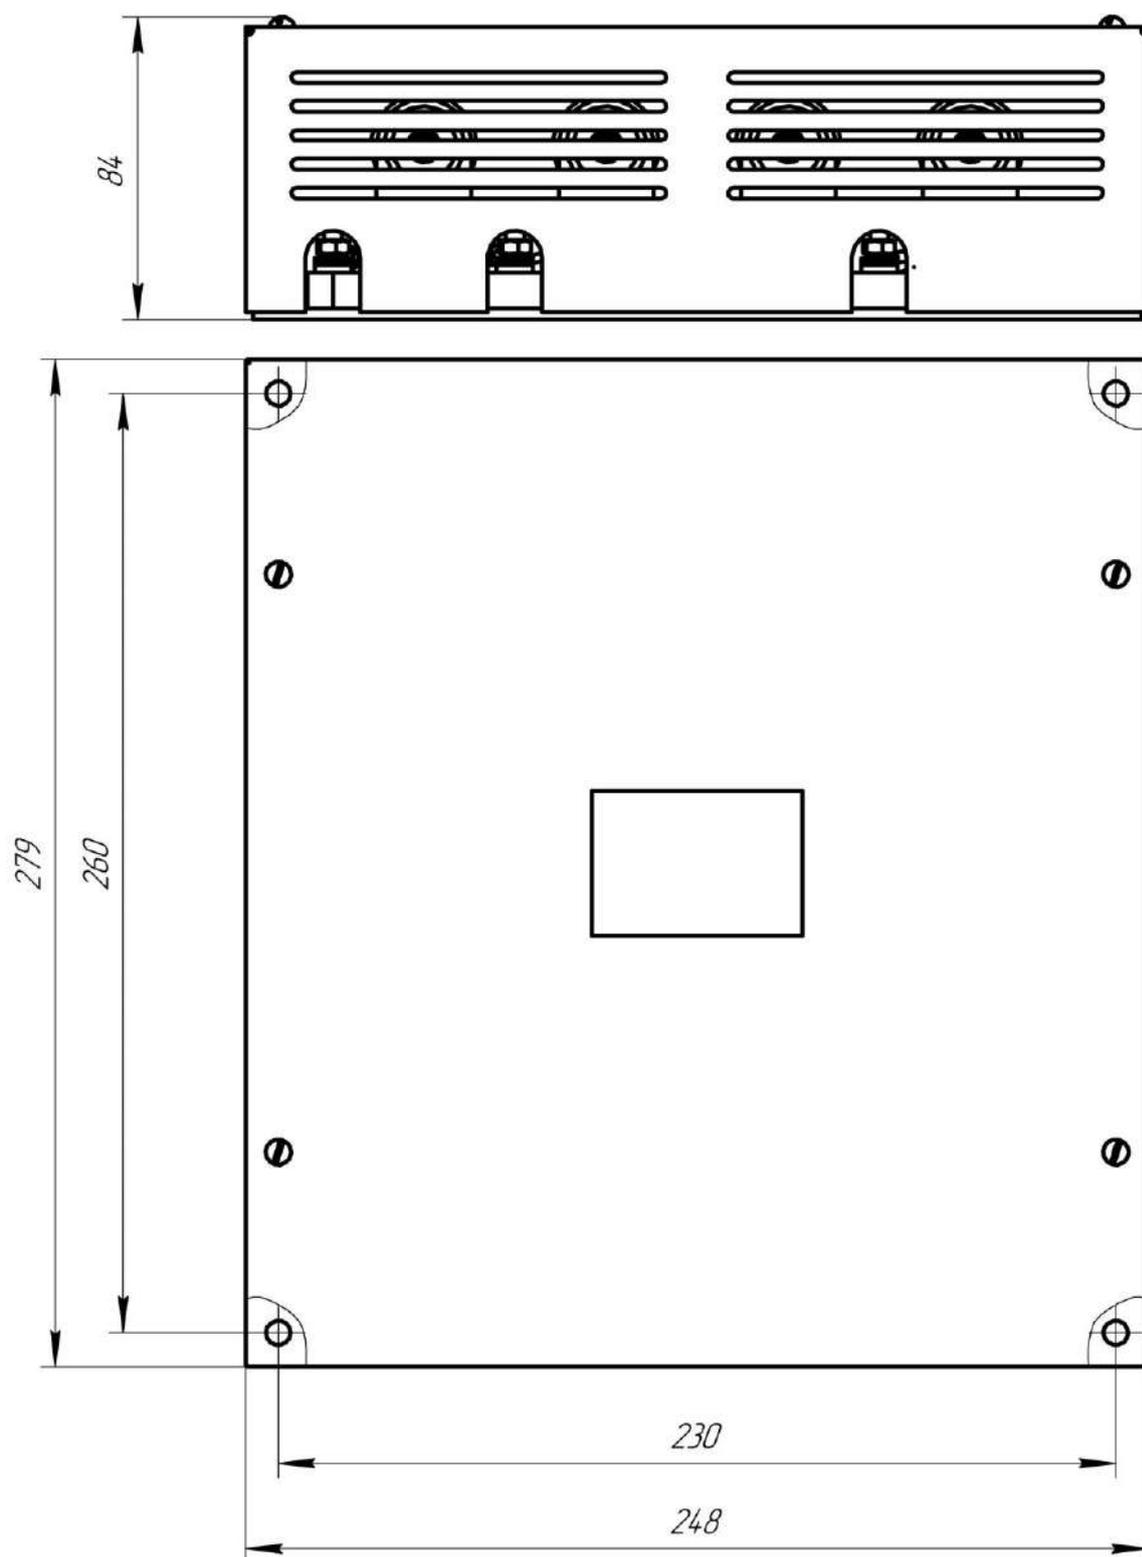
Габаритные и установочные размеры БУП
